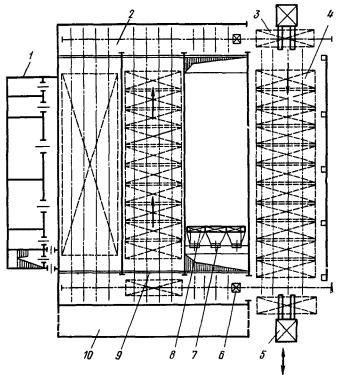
Планировка сушильного цеха с камерами ЦНИИМОД-49:
